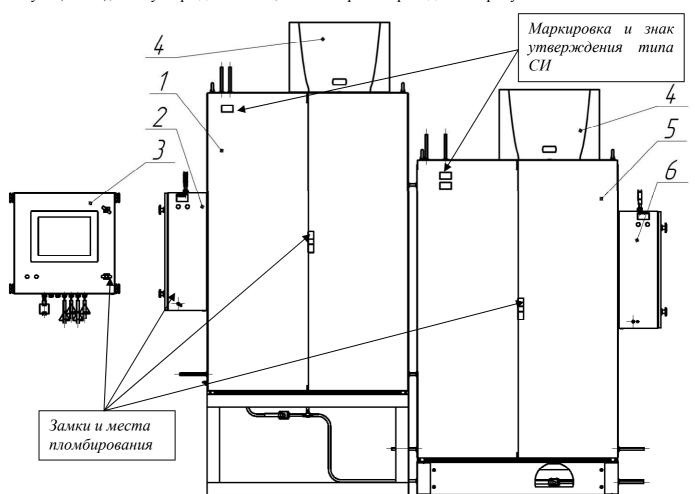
Внешний вид СГЖ и схема пломбировки
